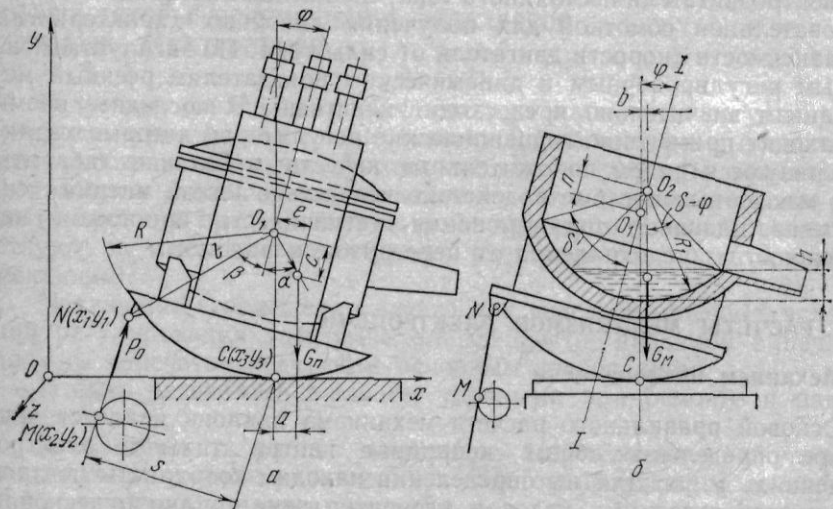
Расчетные схемы к определению опрокидывающих моментов электропечи: a — от веса конструкции печи; b — от веса жидкого металла
